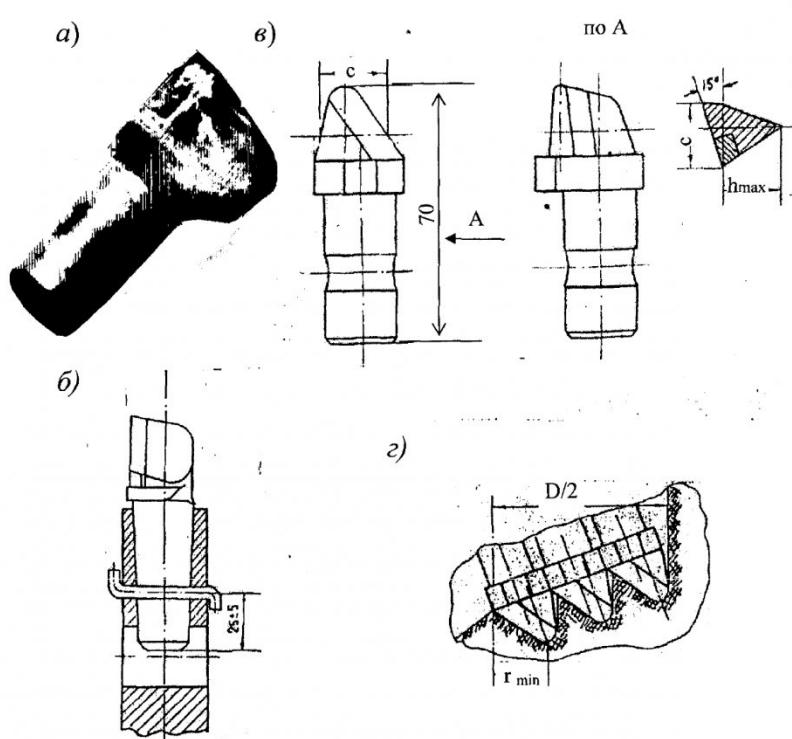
Резцы КузГТУ для режущих буровых долот: а - резец с укороченной цилиндрической державкой; б - крепление резца с цилиндрической державкой на корпусе долота; в - резец КузГТУ с цилиндрической державкой с частичной армировкой передней грани твёрдым сплавом; г - схема работы резцов долота, установленных наклонно
